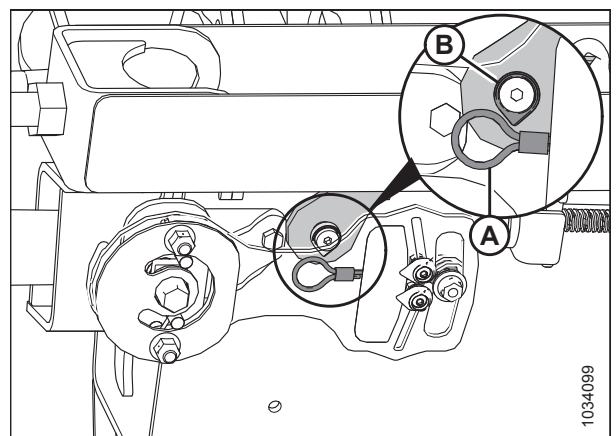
Trava do cabo Flex Checker – Esquerdo
